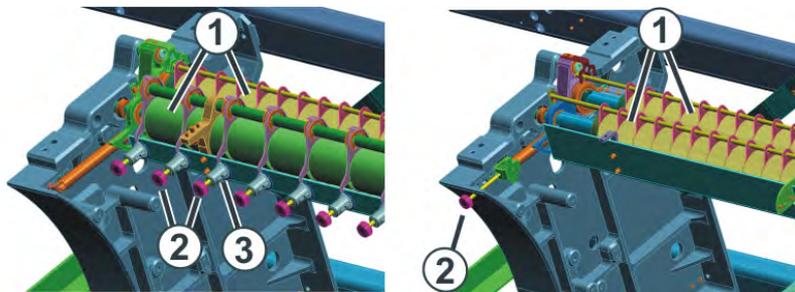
Hauptabzug (rechtes Bild: CMS 502)
